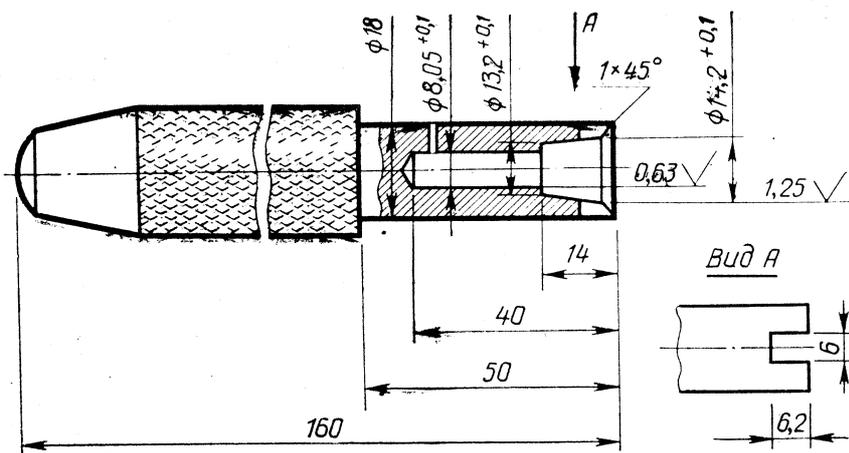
Оправка для установки маслоотражательных колпачков клапанов
